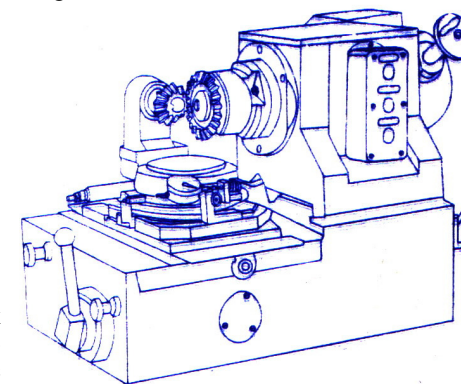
Автоматизированный прибор двухпрофильного контроля для конических зубчатых колес конструкции МПКТИ
